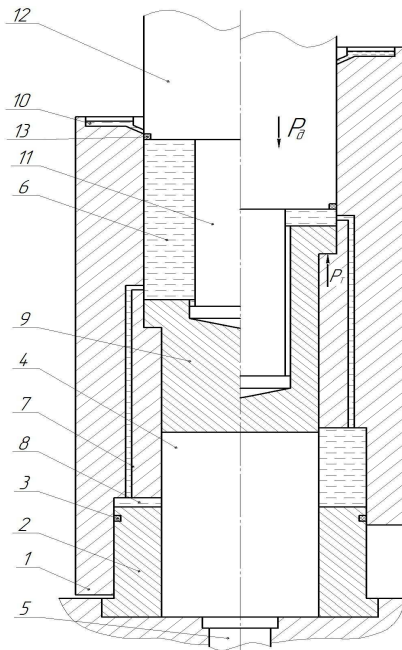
Схема ХВ з розтягненням стінки заготовки.
